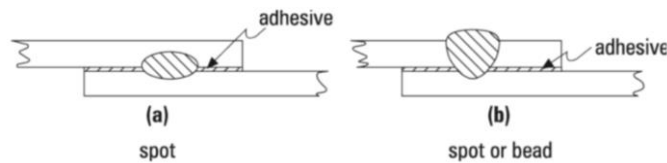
Diferentes métodos de ligação soldada a) soldadura por pontos b) soldadura por cordão [67]
